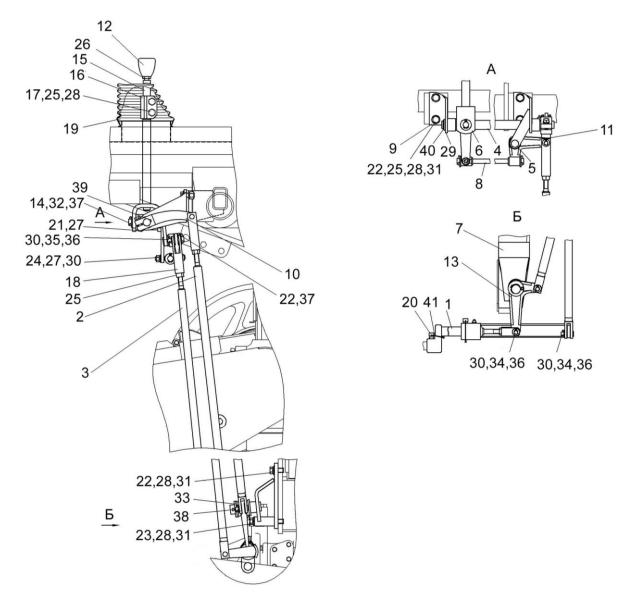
Установка механизма управления коробкой диапазонов КЗК-10-0119040А
